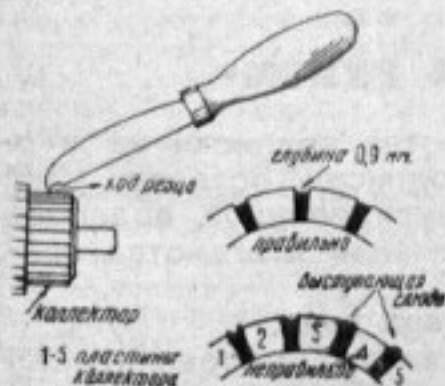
Фрезеровка изоляции между пластинами коллектора
